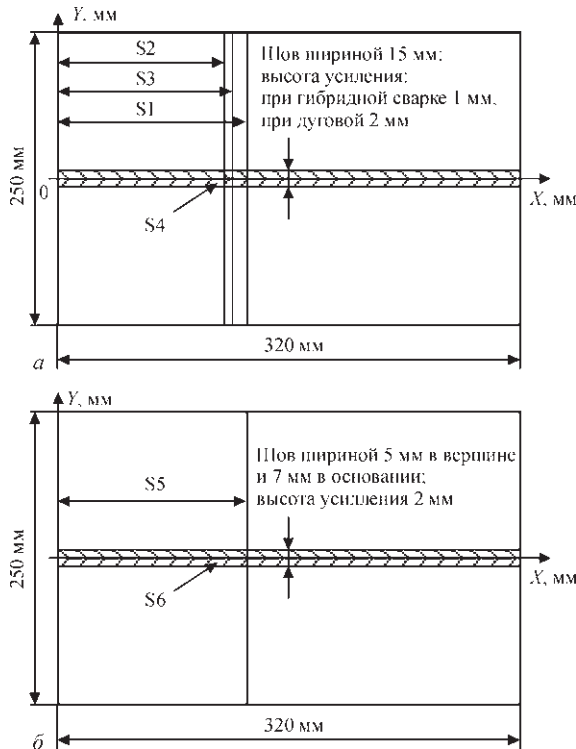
Схемы измерения остаточных напряжений на стыковых сварных соединениях алюминиевого сплава 1561, выполненных дуговой и гибридным способами: а — лицевая (верхняя) сторона, сечения S1–S3 — измерения поперек шва, S4 — вдоль линии шва; б — обратная (нижняя) сторона, сечение S5 — поперек шва, S6 — вдоль шва; по оси X сечения расположены на расстоянии: S1 — 166, S2 — 148, S3 — 155, S5 — 168 мм; по оси Y сечения S4 и S6 проходили по нулевой отметке
